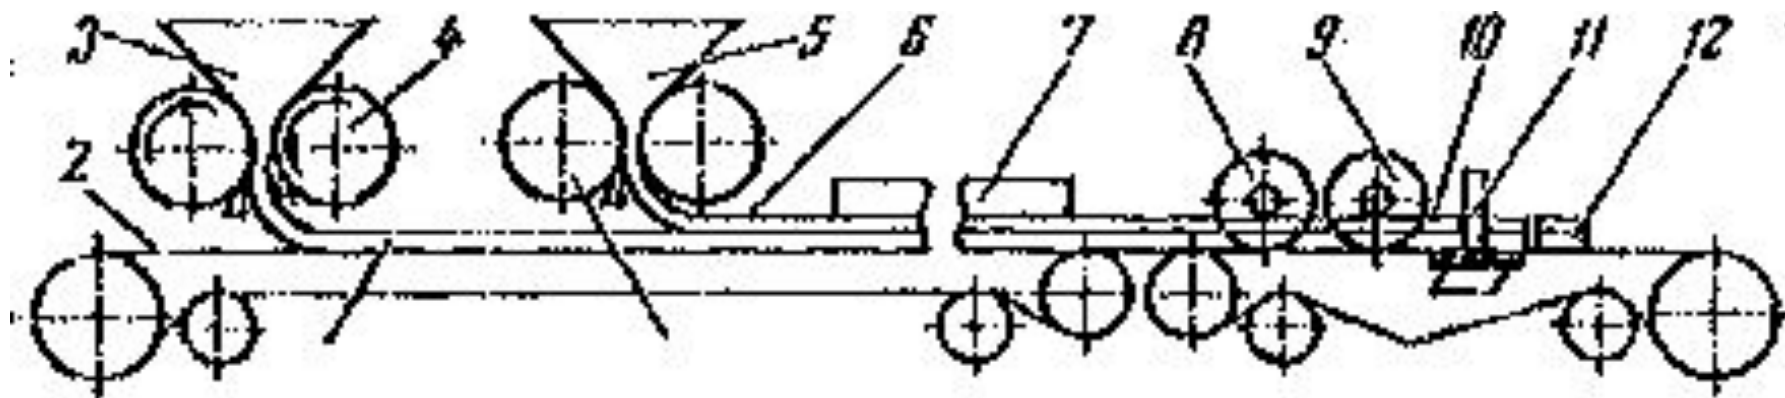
Схема формования конфетных корпусов раскаткой и резкой
